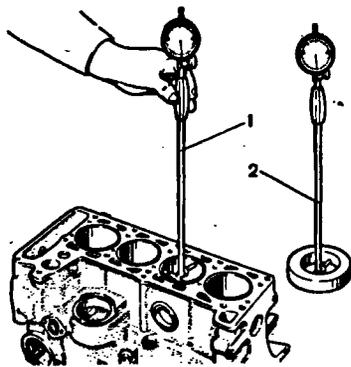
Измерение цилиндров нутромером: 1 - нутромер; 2 - установка нутромера на ноль по калибру А.96137
